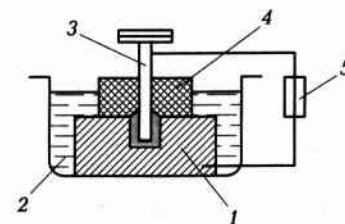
Схема установки для электроискрового прошивания отверстий
